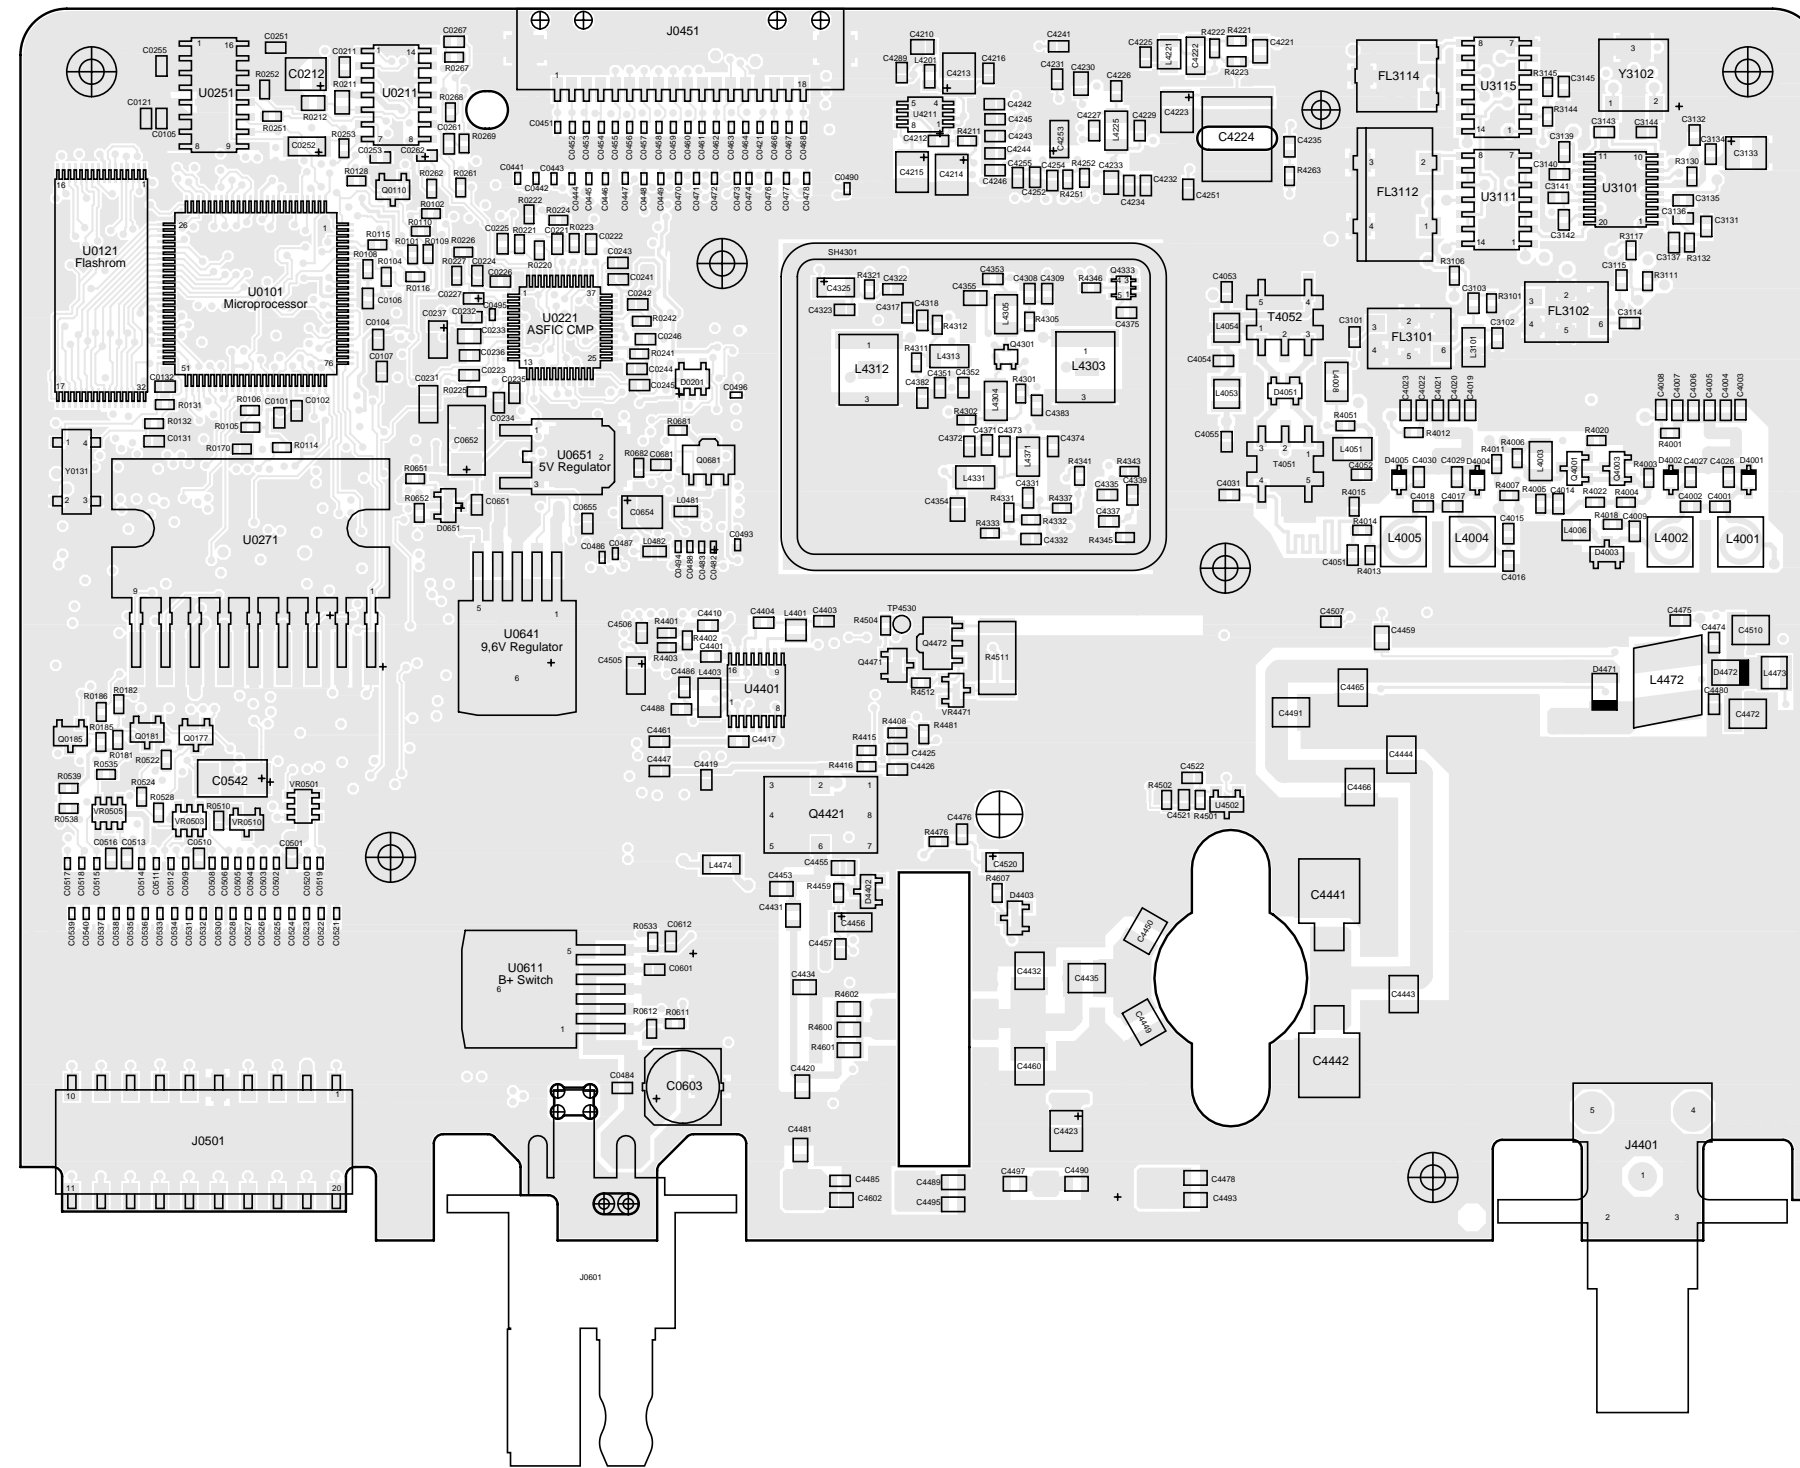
PCB del lado superior de la tarjeta principal de UHF (403-470MHz)
